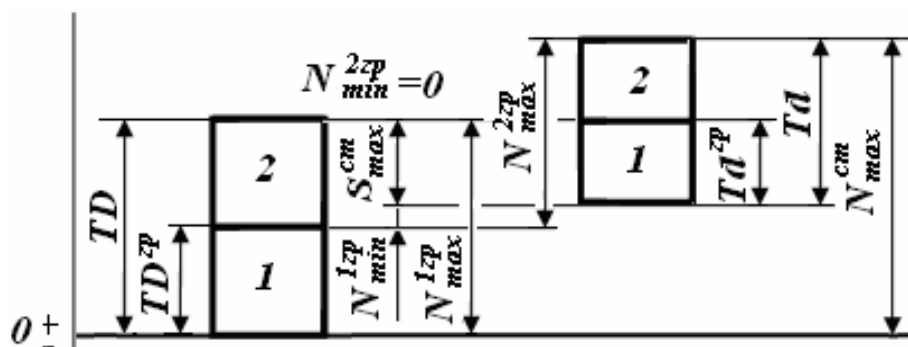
Схеми розташування полів допусків для перехідної посадки
